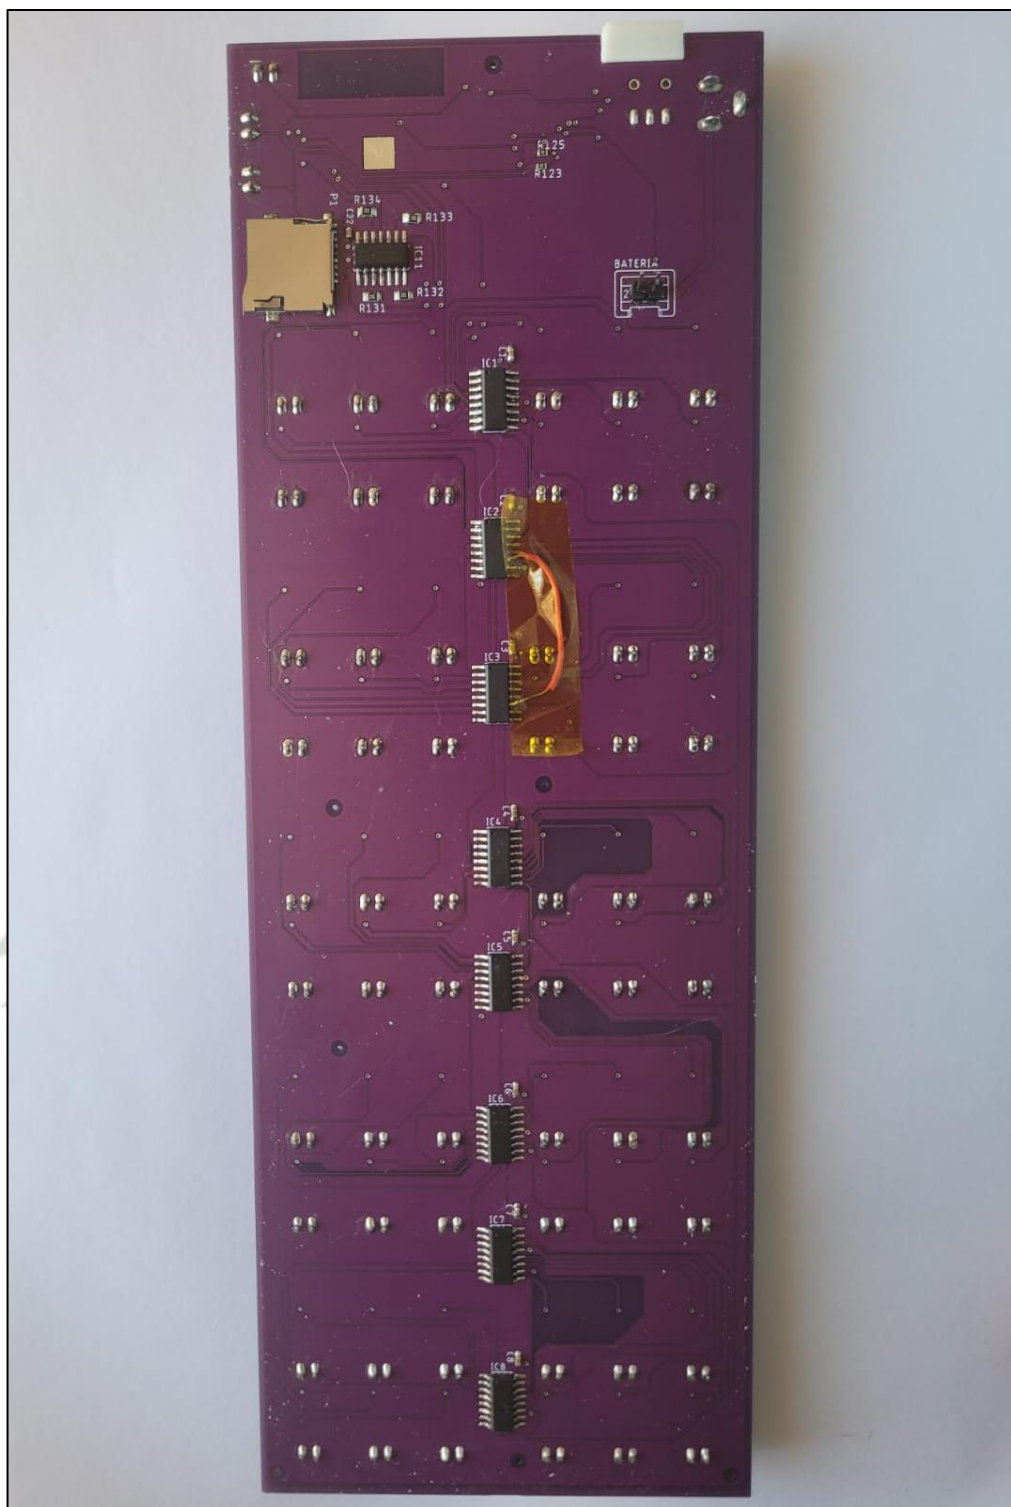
Vista de capa inferior PCB con todos los componentes soldados
